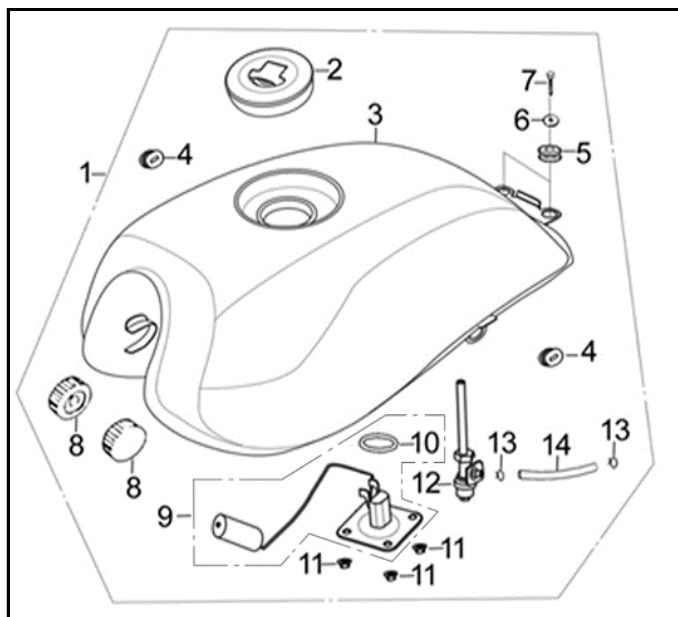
TANQUE DE COMBUSTIBLE
